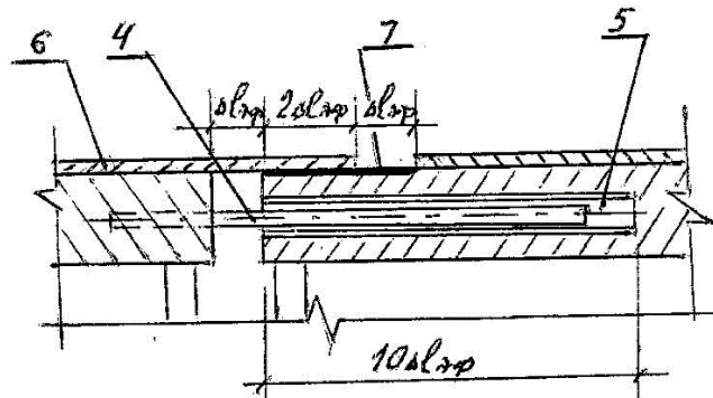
Узел А пальцево-втулочного соединения частей корпуса
